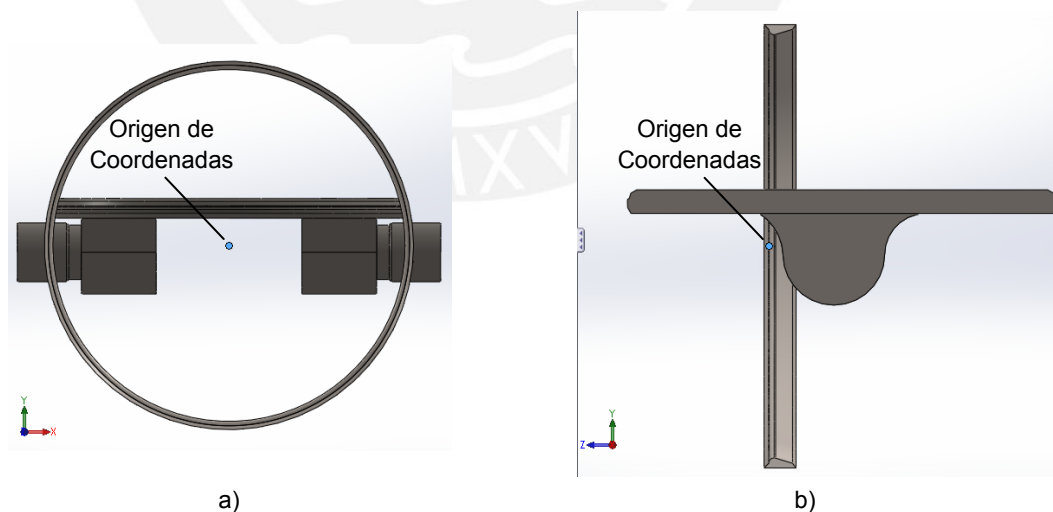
Vistas de la ubicación de los objetos: a) Vista del plano XY b) Vista del plano YZ [Material propio]
